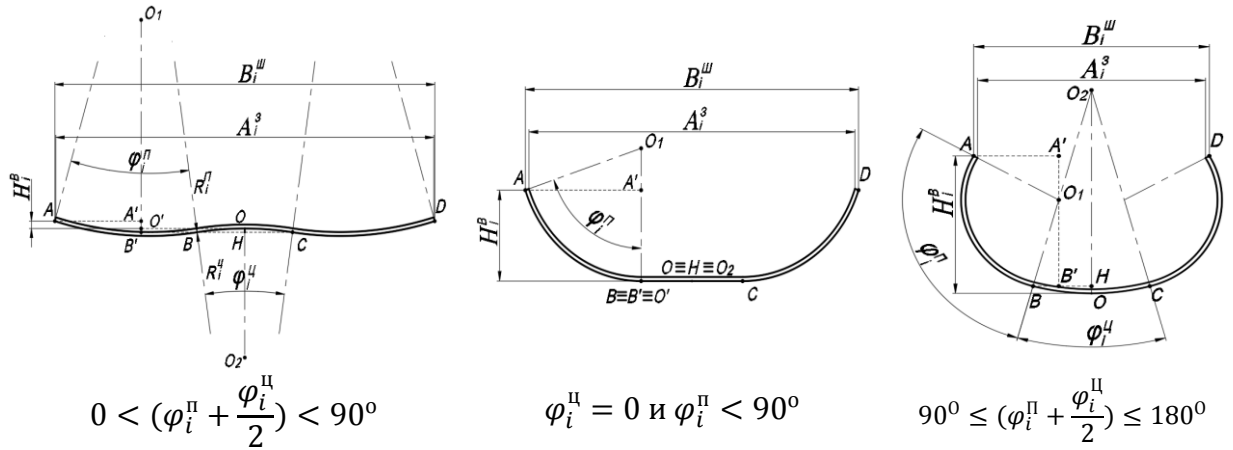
Характерные типы профилей заготовки по длине очага сворачивания ТЗ
